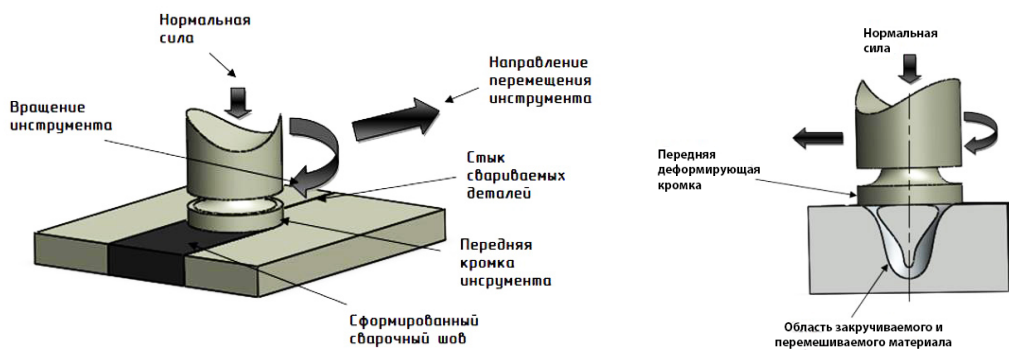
Процесс сварки трением с перемешиванием
